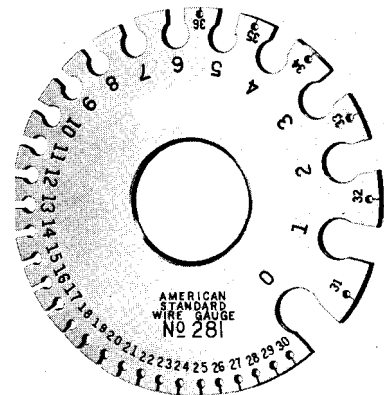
Calibrador de la American Wire Gauge (LS. Starrett Company).
